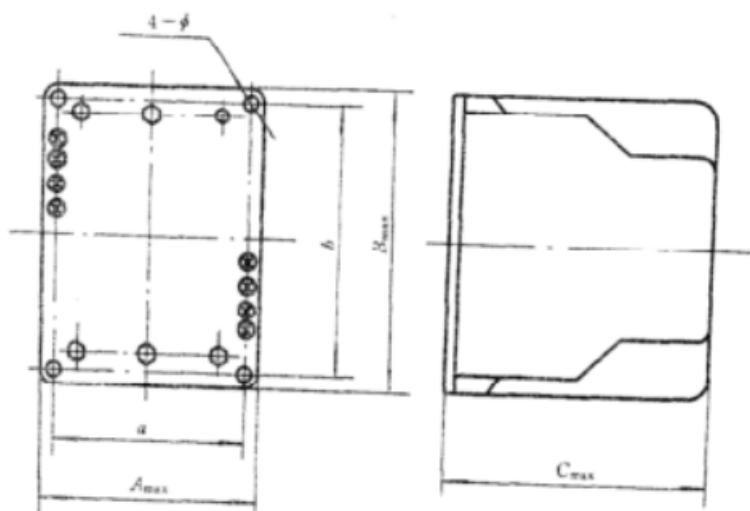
CJX 5-120, 150 型交流接触器外形尺寸与安装尺寸
